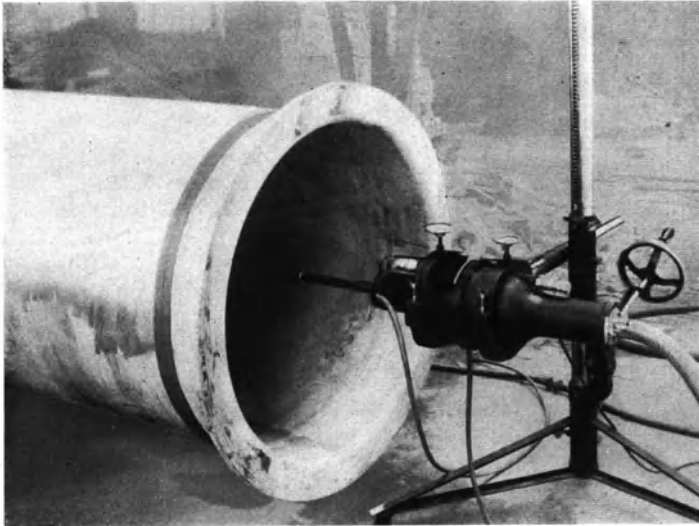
Durchleuchtung der Schweißnaht eines Kessels mittels eingeschobener Röntgenquelle (Endpolröhre) (R. SEIFERT-Hamburg).
